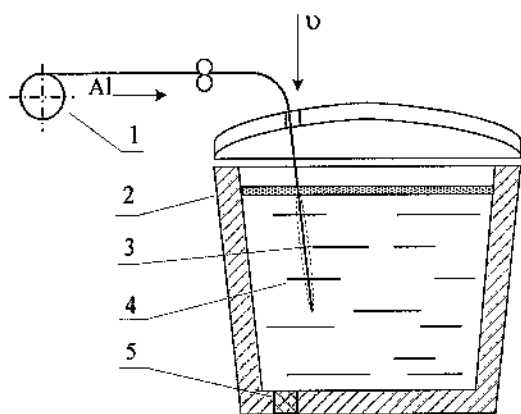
Схема установки ввода алюминиевого прутка в ковш с металлом: 1 - трайб-аппарат; 2 - ковш с жидким металлом; 3 - цилиндрический алюминиевый пруток; 4 - расплав; 5 - пористая вставка для подачи аргона; v - скорость движения прутка
